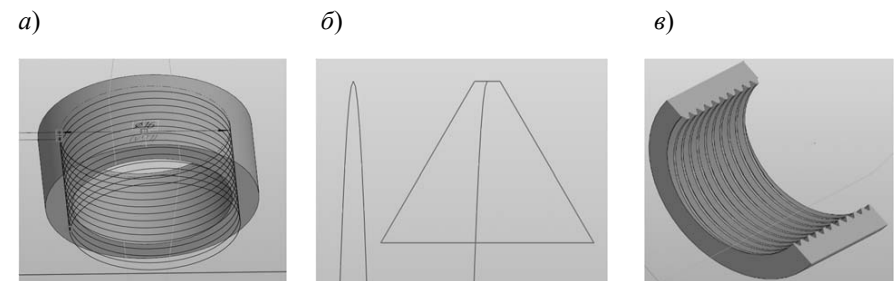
Порядок построения резьбы в цилиндрическом отверстии
